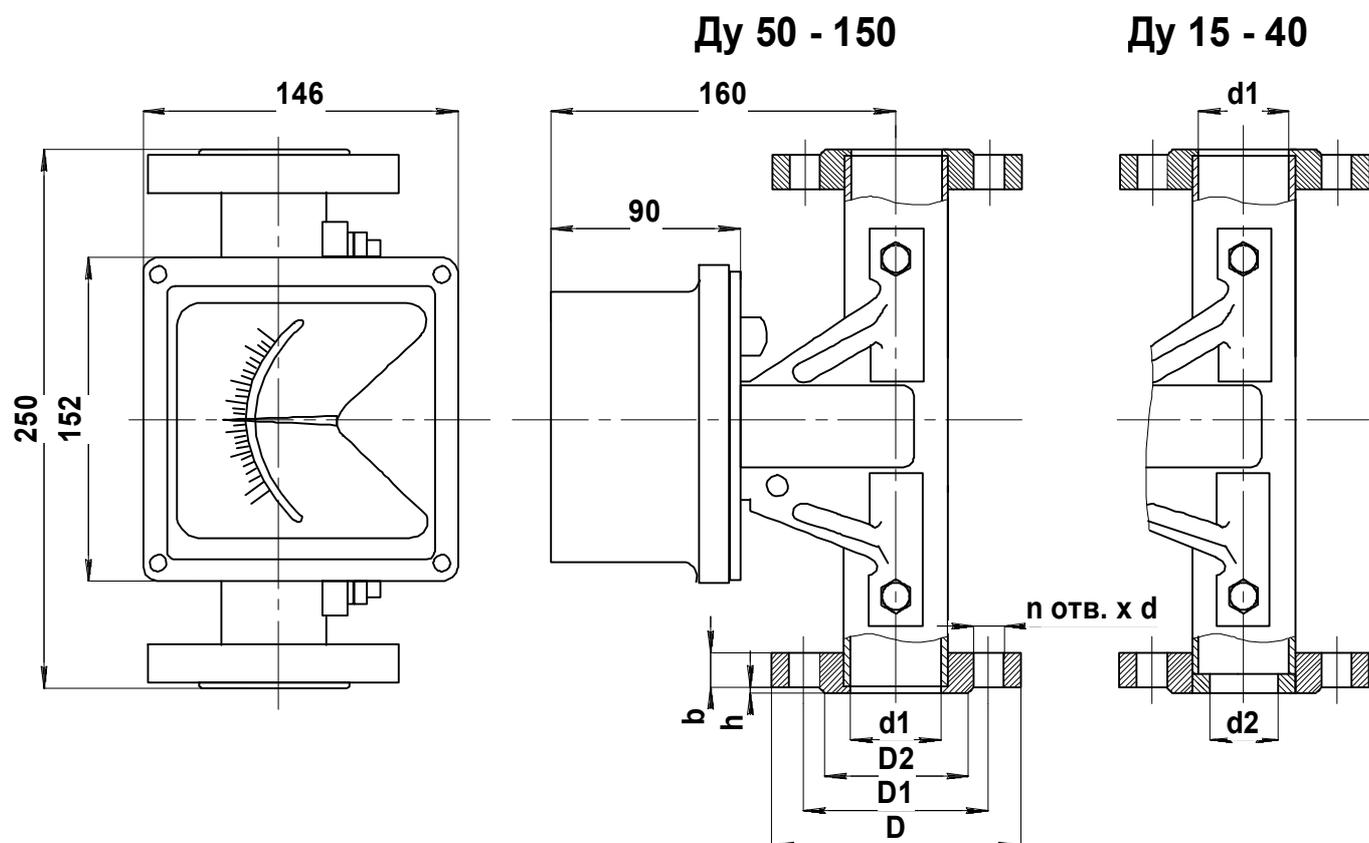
Габаритные и присоединительные размеры ротаметров с фланцевым соединением
